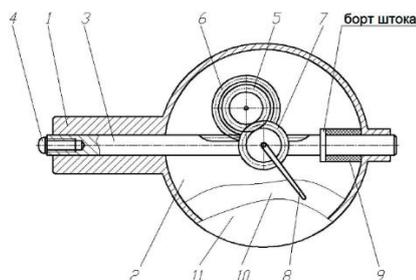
Схема устройства: 1 – корпус, 2 – крышка, 3 – рейка, 4 – индентор, 5 – реечное зубчатое колесо, 6 – передаточное зубчатое колесо, 7 – трибка, 8 – стрелка, 9 – упругая вставка из резины, 10 – циферблат; 11 – защитное стекло [7]
